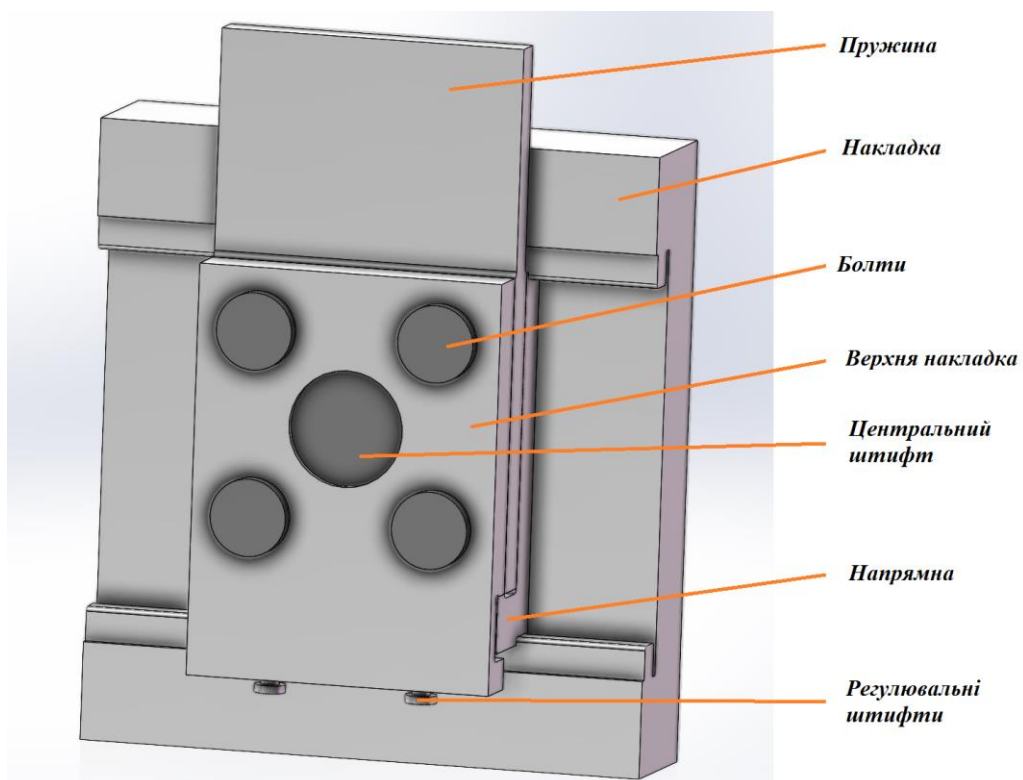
Тривимірне зображення вузла кріплення пружини до корпусу статора
